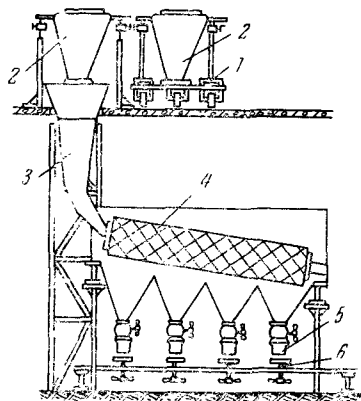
Схема механического сита: 1 — тележка; 2 — бункер с исходным порошком; 3 — направляющий конус; 4 — наклонный вращающийся барабан с металлической сеткой; 5 — сборник порошка; 6 — прижимной винт
